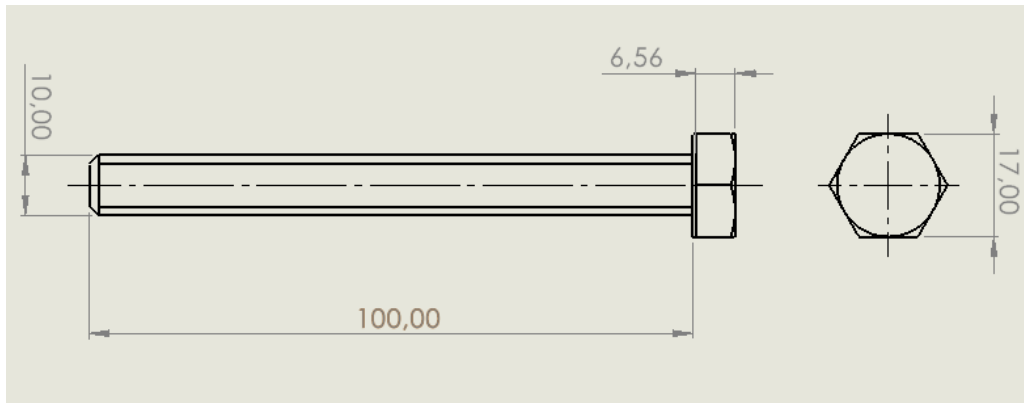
Desenho técnico das vistas frontal e lateral do parafuso, com suas dimensões em milímetros. (OS AUTORES, 2022).
